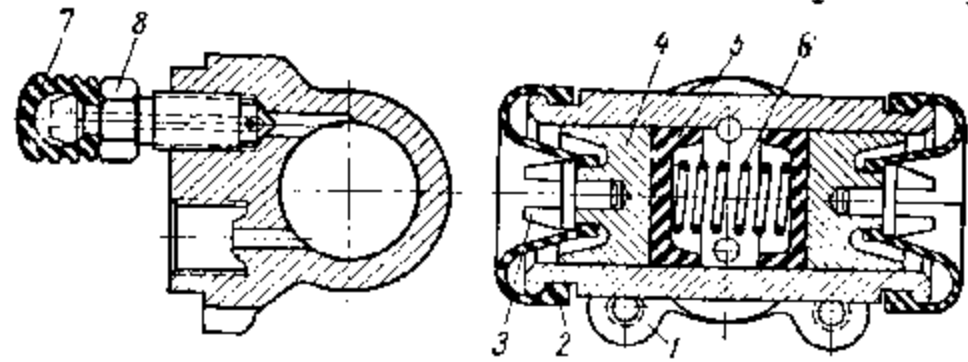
Колесный цилиндр тормоза переднего колеса:
